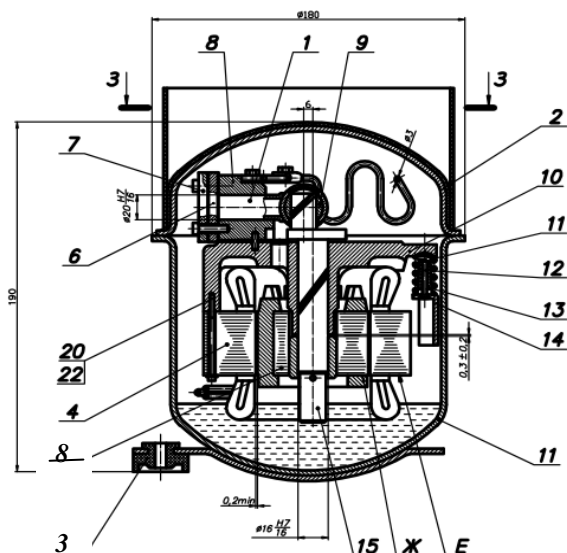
Устройство герметичного компрессора бытовой холодильной машины: 1 – поршень; 2 – крышка кожуха; 3 – амортизатор; 4 – обмотка статора; 5 – ротор; 6 – клапанная плита; 7 – крышка головки; 8 – шпилька; 9 – ползун кулисы; 10 – статор; 11 – прокладка; 12 – шпилька подвески; 13 – пружина подвески; 14 – кронштейн подвески; 15 – шейка вала.
